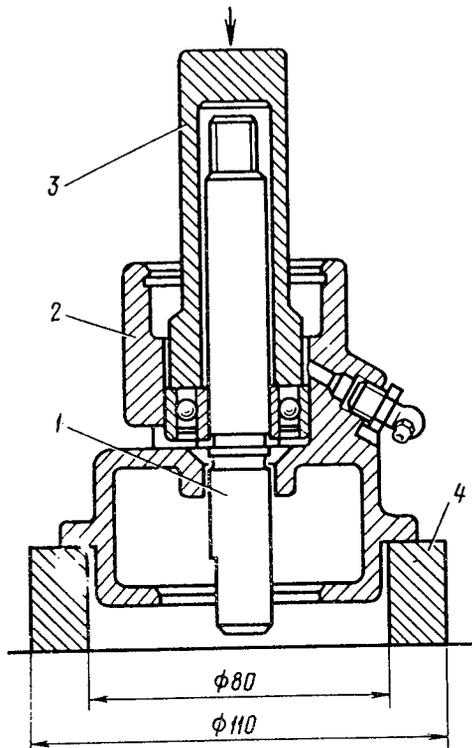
Einpressen der Welle zusammen mit Lager in das Wasserpumpengehäuse:
